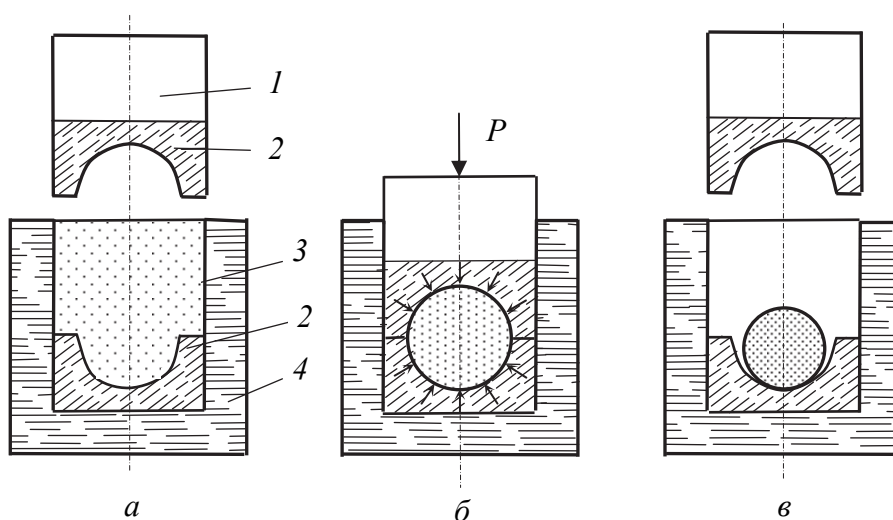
Схема квазиизостатического прессования сферической заготовки:
